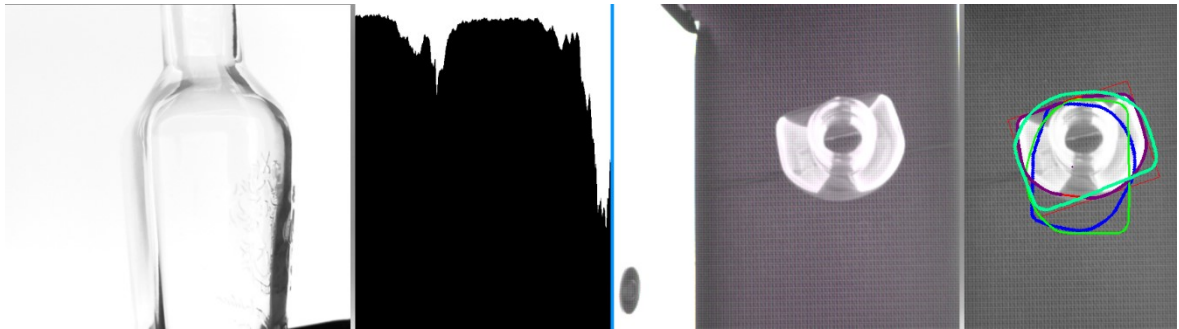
Teste com garrafa 3 em movimento e 140° de rotação.
